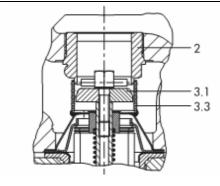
Принцип действия, универсальный редуктор давления тип 41-23
